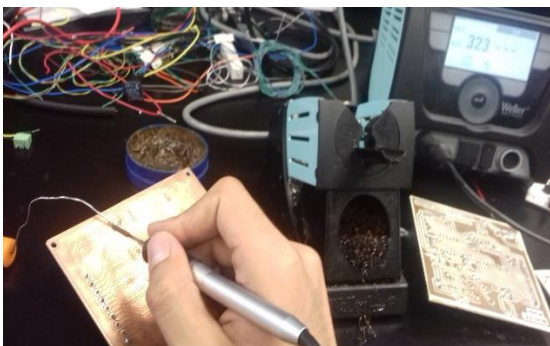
Soldado de placa con Estación Weller
